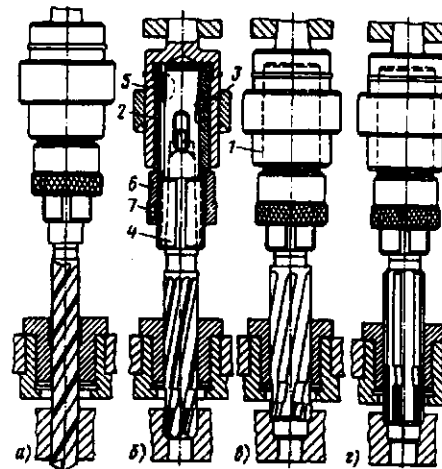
Схемы последовательной обработки (а – г) заготовки на одношпиндельном сверлильном станке: 1 – быстросменный патрон; 2 – промежуточная втулка; 3 – винт; 4 – регулируемая втулка; 5 – сегментная шпонка; 6 – гайка; 7 – винт
